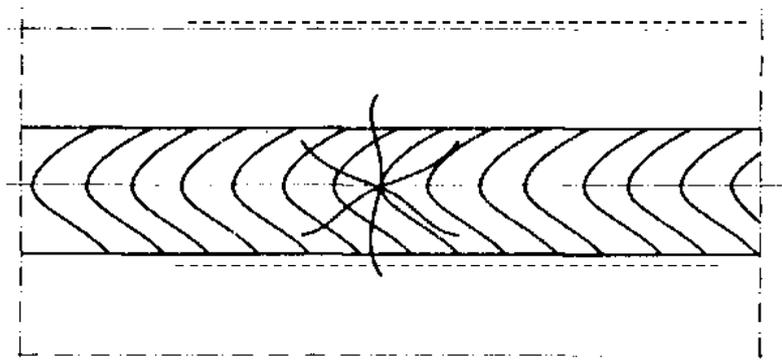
Радиальная трещина сварного соединения
